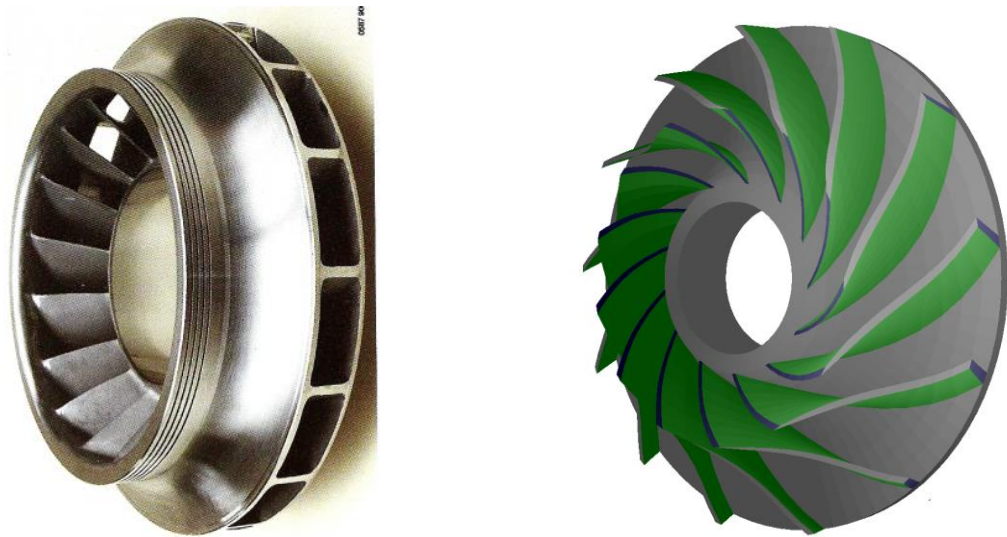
Внешний вид закрытого осерадиального рабочего колеса с пространственными лопатками и схема его лопаточной решетки (покрывающий диск снят)
